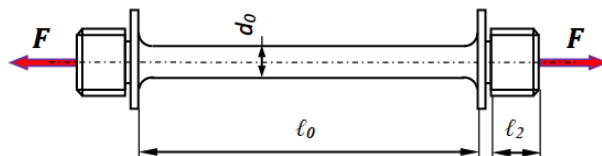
Ескіз зразка для випробувань на ударний розтяг.
